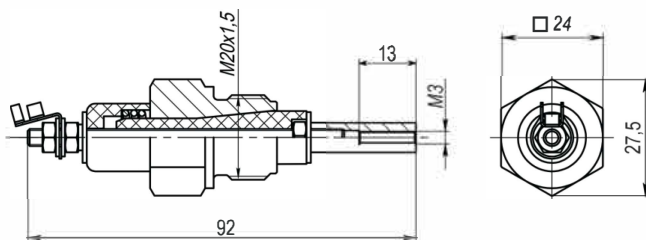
габаритные и установочные размеры датчика КДУ-1Э
